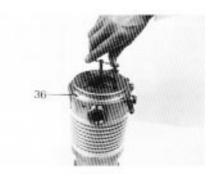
Motor-Lagerschild 36 lösen Loosen motor part 36 Desserrer le flasque du moteur 36
